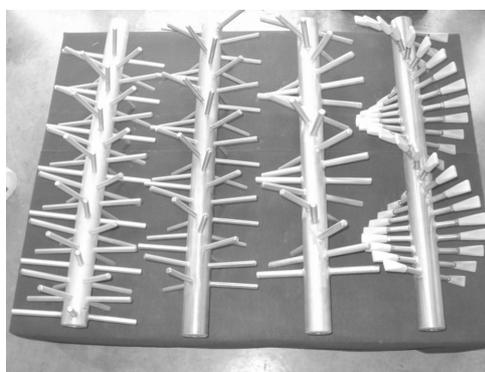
Verschiedene Stift- und Fingerwellen für ZICKLER-RAUCH Abbeermaschinen
